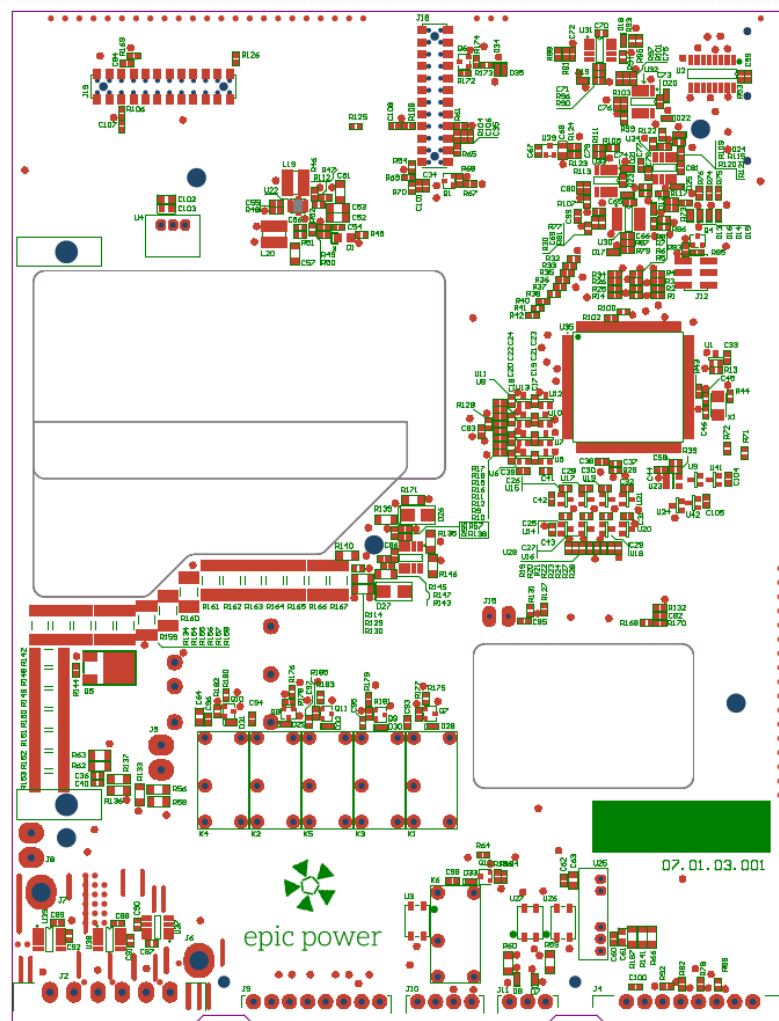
EJEMPLO DE PCB DISEÑADA PARA EL CONVERTIDOR
